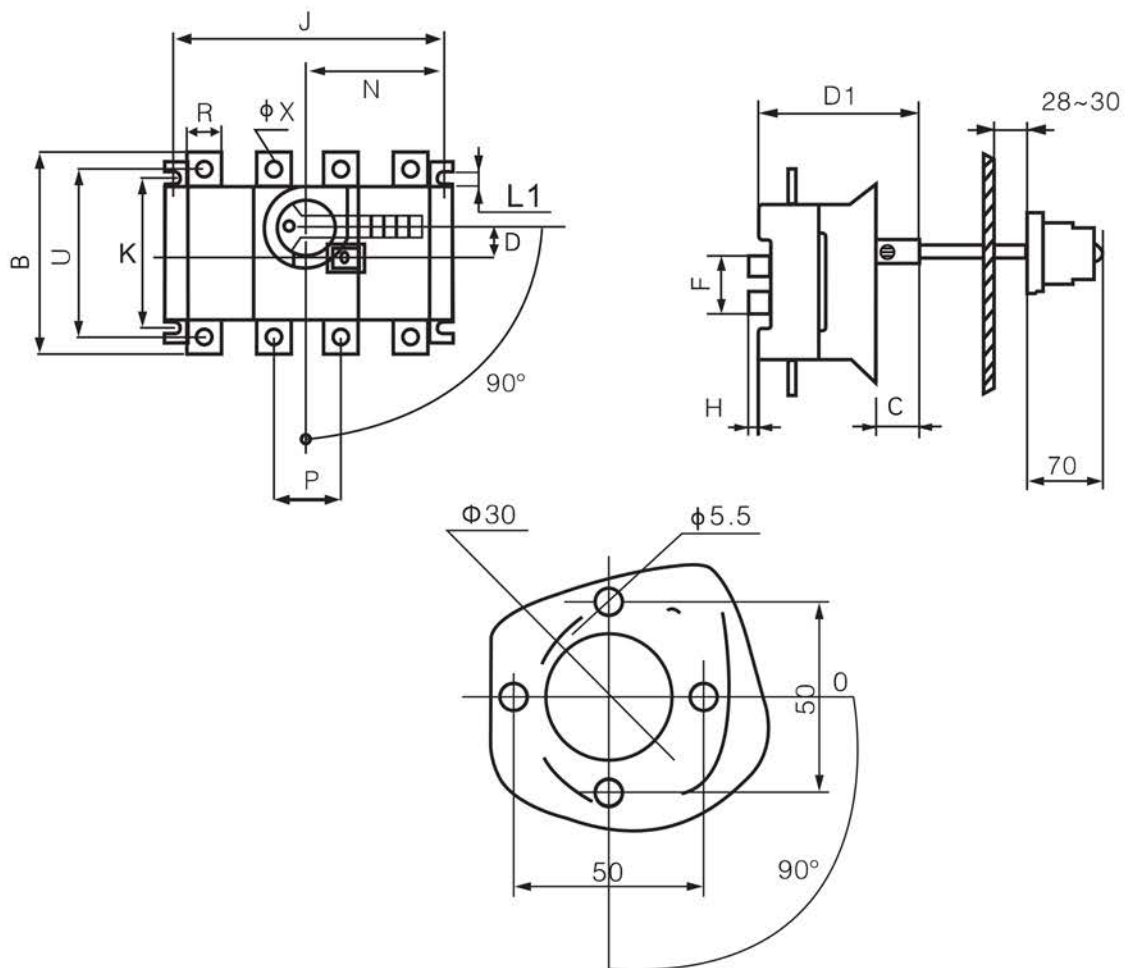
а – Монтажные размеры рубильника PowerSwitch 400-630 А
